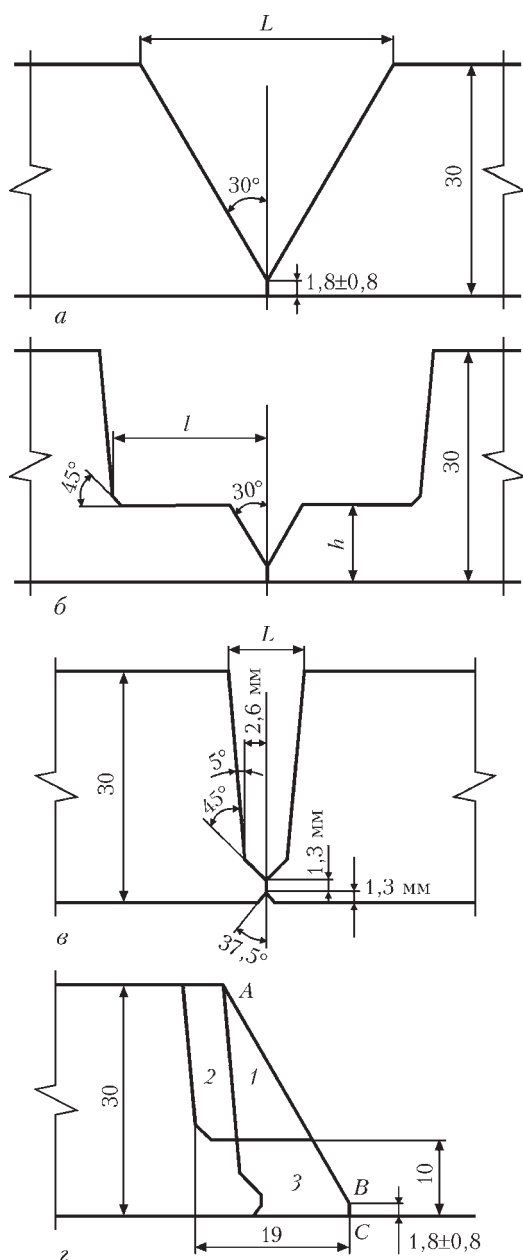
Схемы разделки кромок: для ручной электродуговой сварки (а); КСО (б); CRC (в); совмещенные схемы (г)
